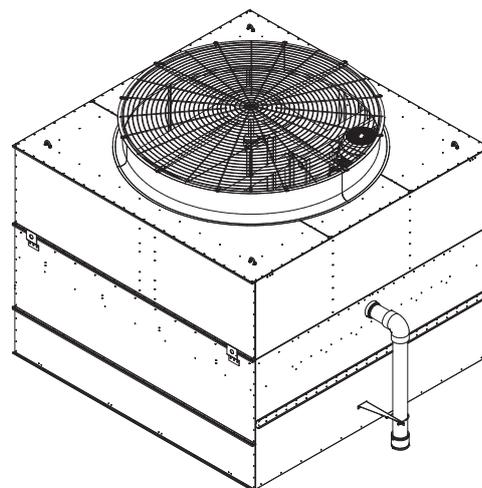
Sezione ventilante pronta per il montaggio sulla sezione bacino
